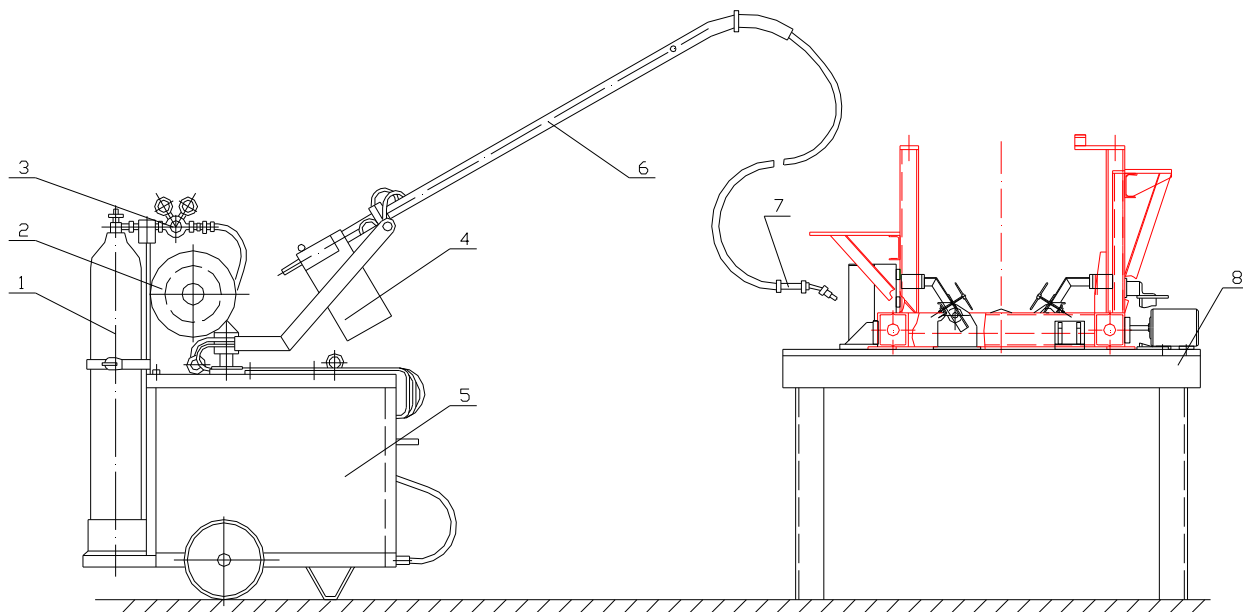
Установка для сварки рамы и приваривание стоек.
